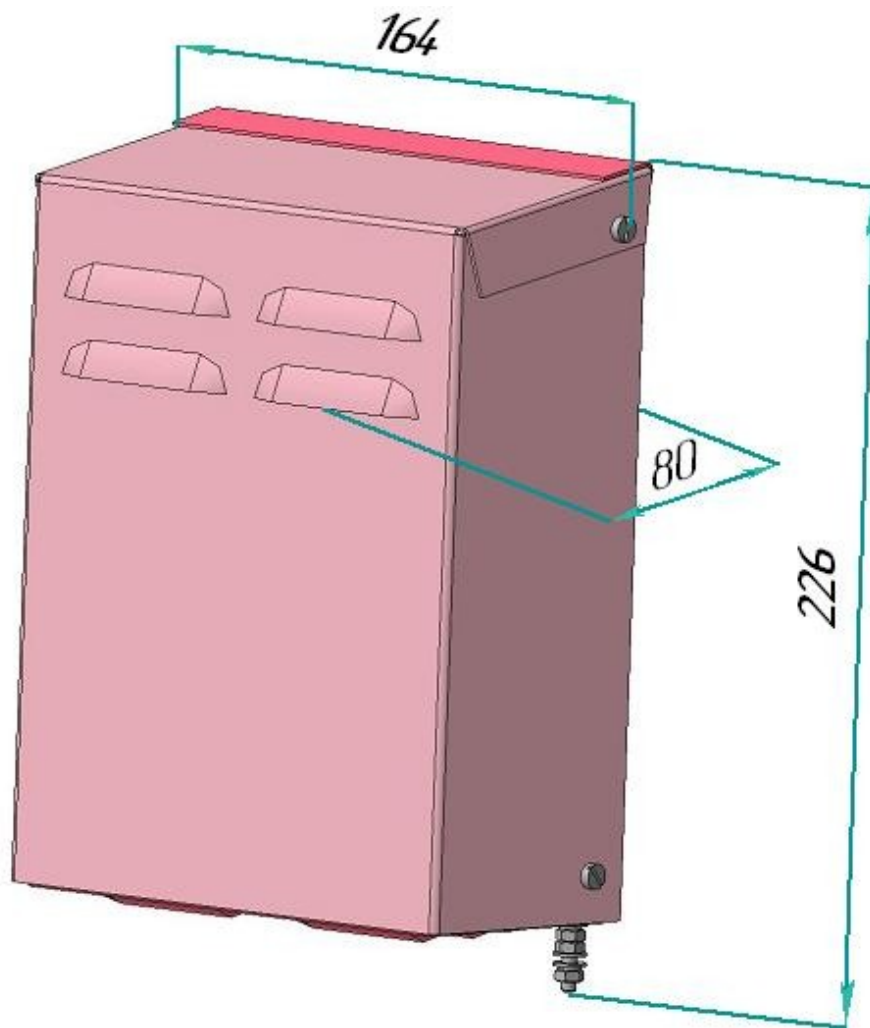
Внешний вид и габариты корпуса для АЛС-АУ
